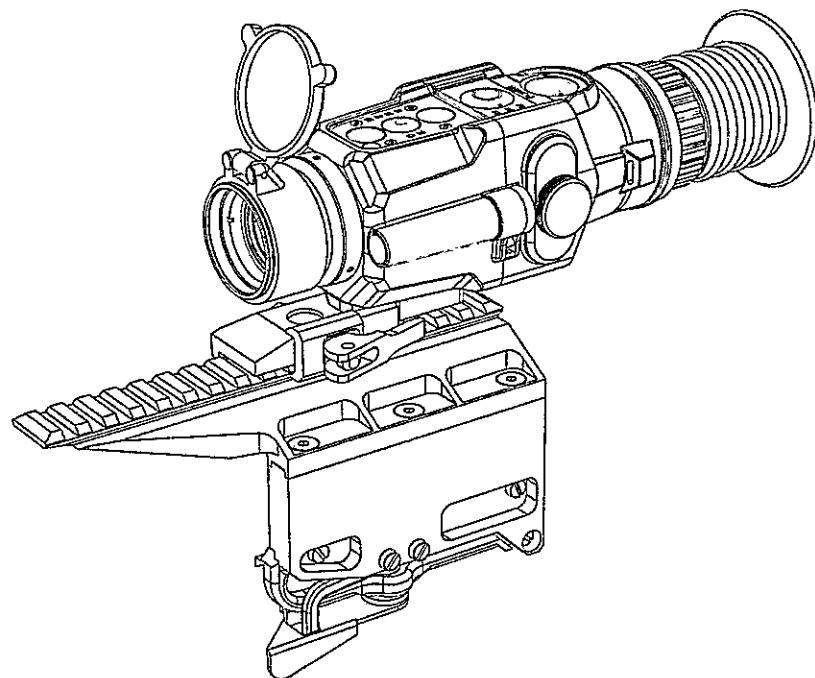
Изделие с боковой планкой крепления SMN WP-2525
